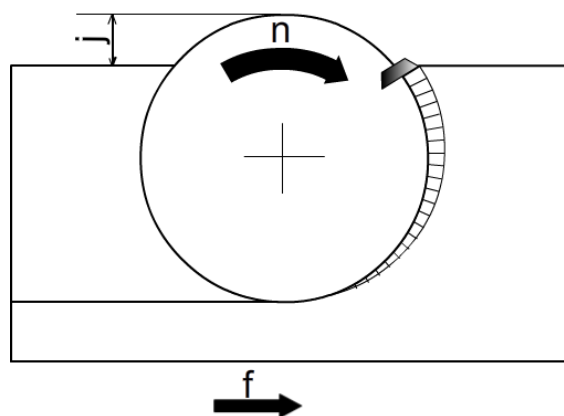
Posición de la herramienta en la pieza para un fresado frontal asimétrico
